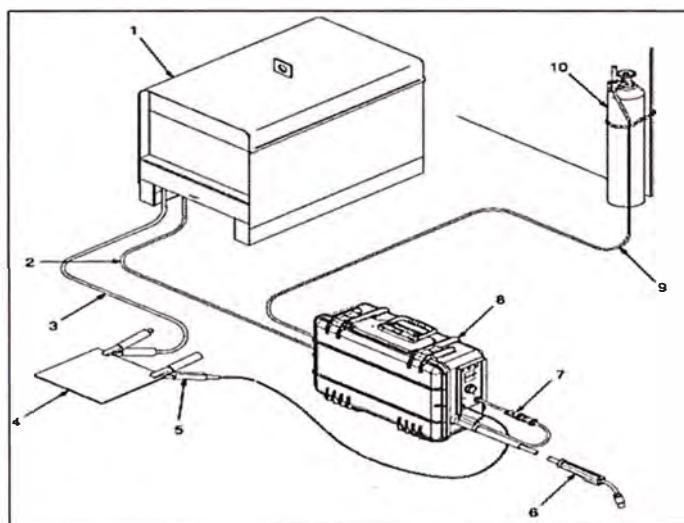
Esquema de soldadura Convencional GMAW.
